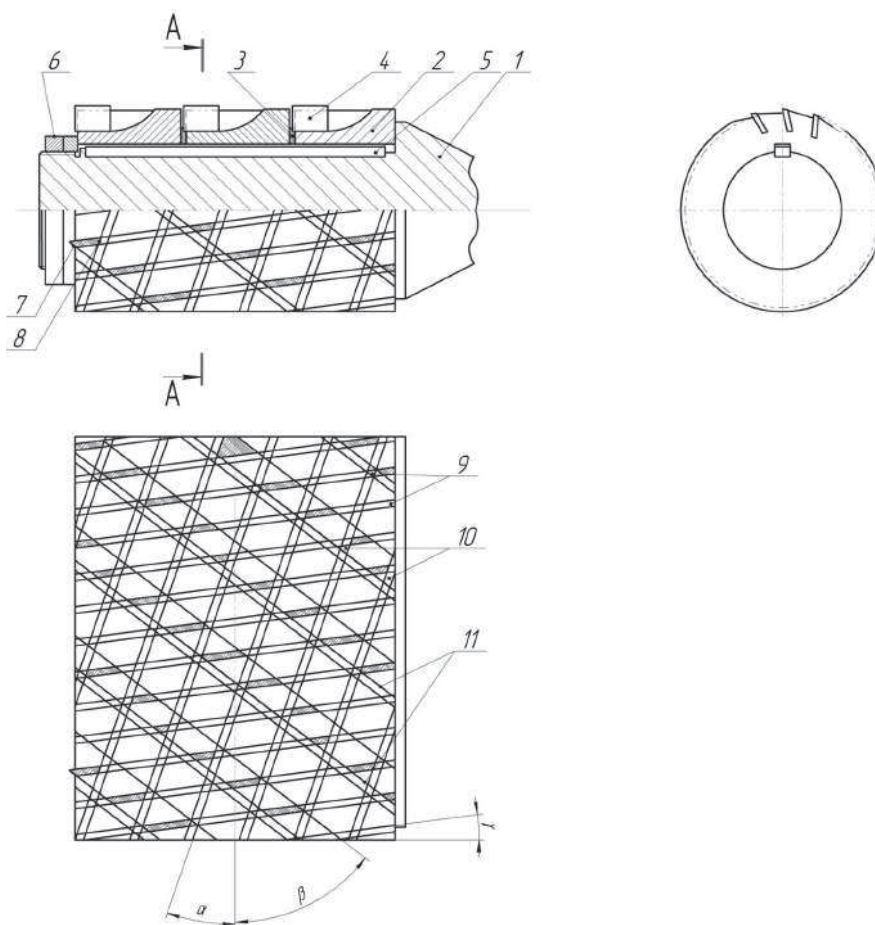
Вид цилиндрической фрезы с разверткой наружной поверхности
